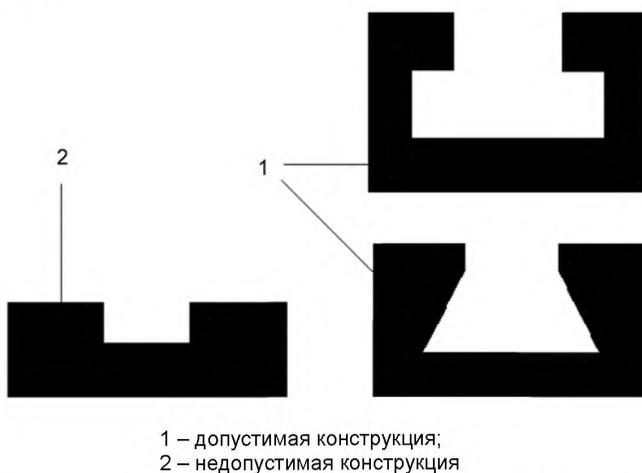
Образцы используемой формы для крепления поперечного упора
